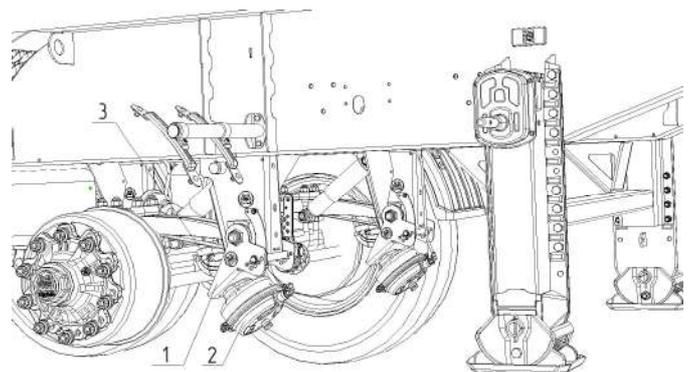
Двухсторонний механизм подъёма оси с пневмцилиндром.
